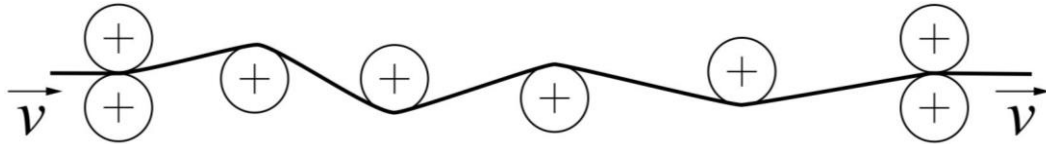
Схема деформации изгиба заготовки при ее движении через систему роликов
